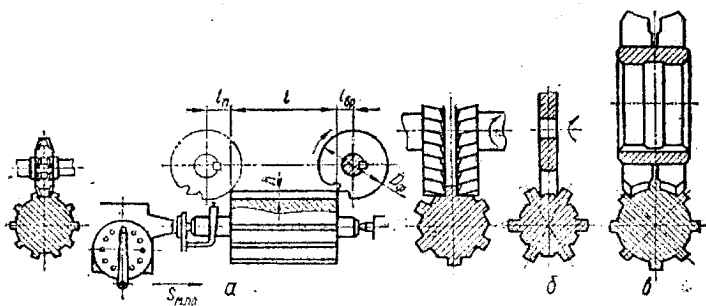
Фрезерування шліцьових пазів копіюванням
